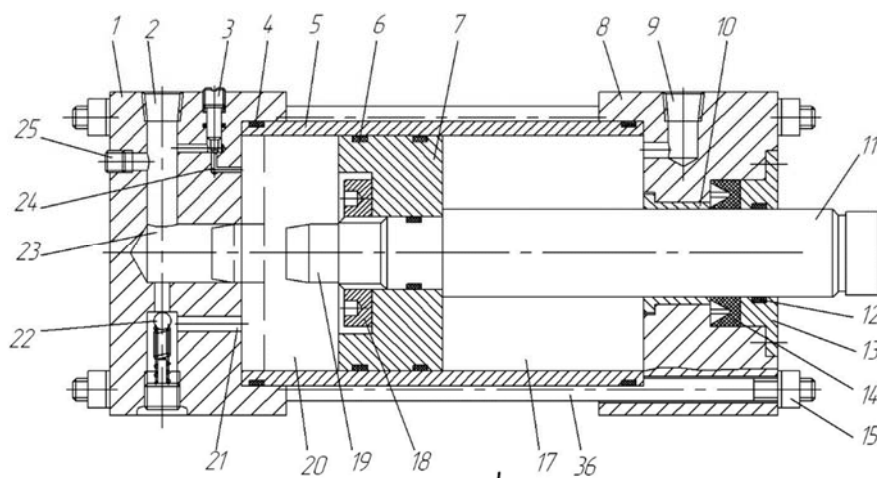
Конструкция одноштокового гидроцилиндра
